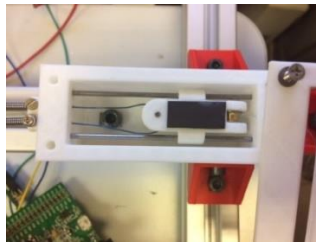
Pieza 2 extremo actuador vista superior.
